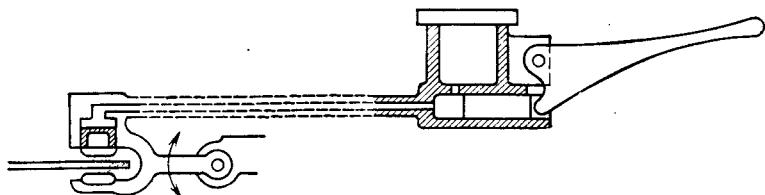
Схема привода дискового тормоза с однопоршневой скобой
